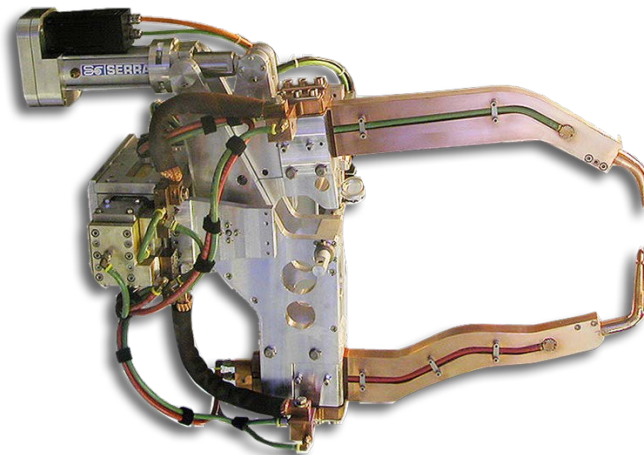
Pinça de soldadura amb accionament elèctric. Font: Serra Soldadura S.A.
